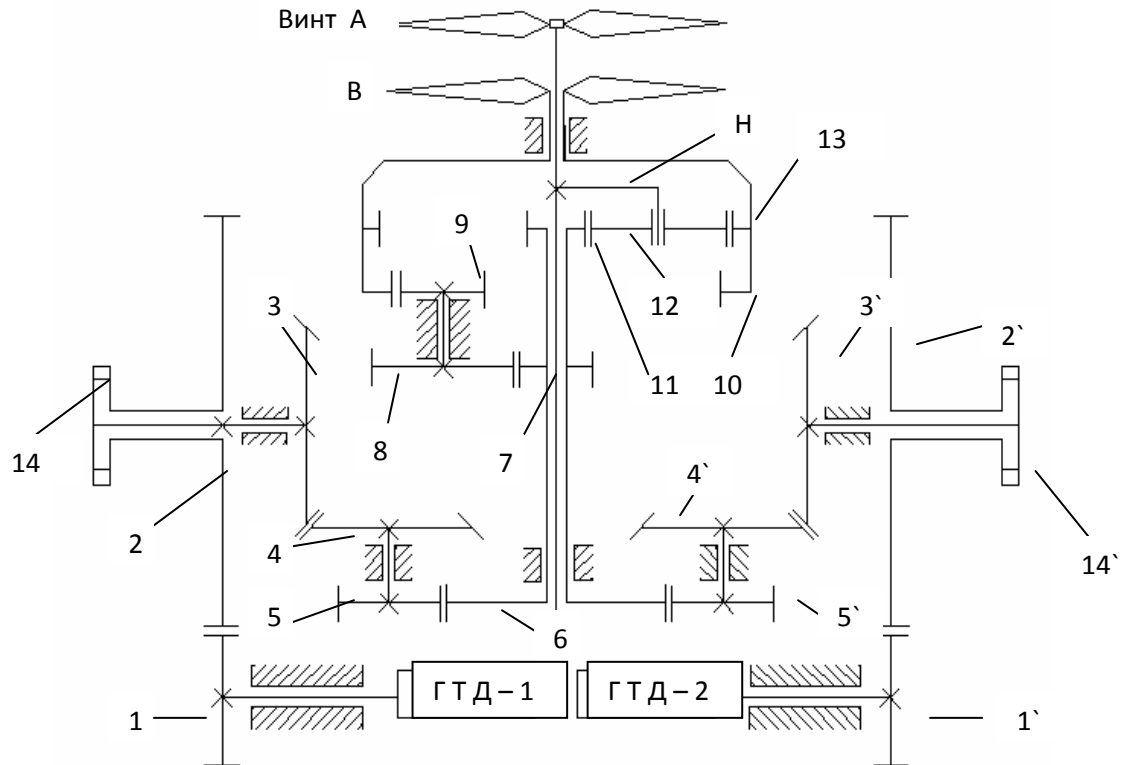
Кинематическая схема редуктора ВР – 3Ф:
